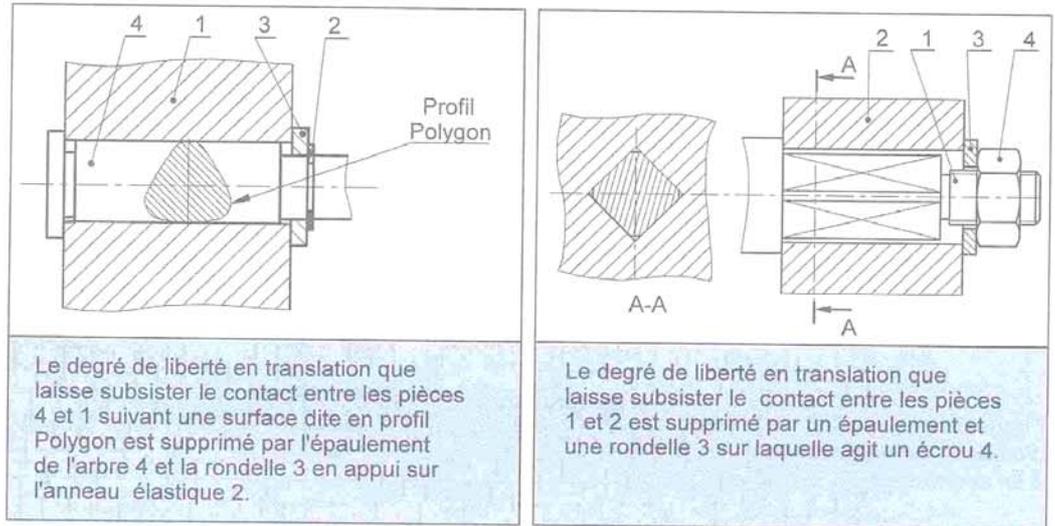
Exemples de solutions constructives réalisant un assemblage démontable par utilisation de surfaces cylindriques ou prismatiques.
